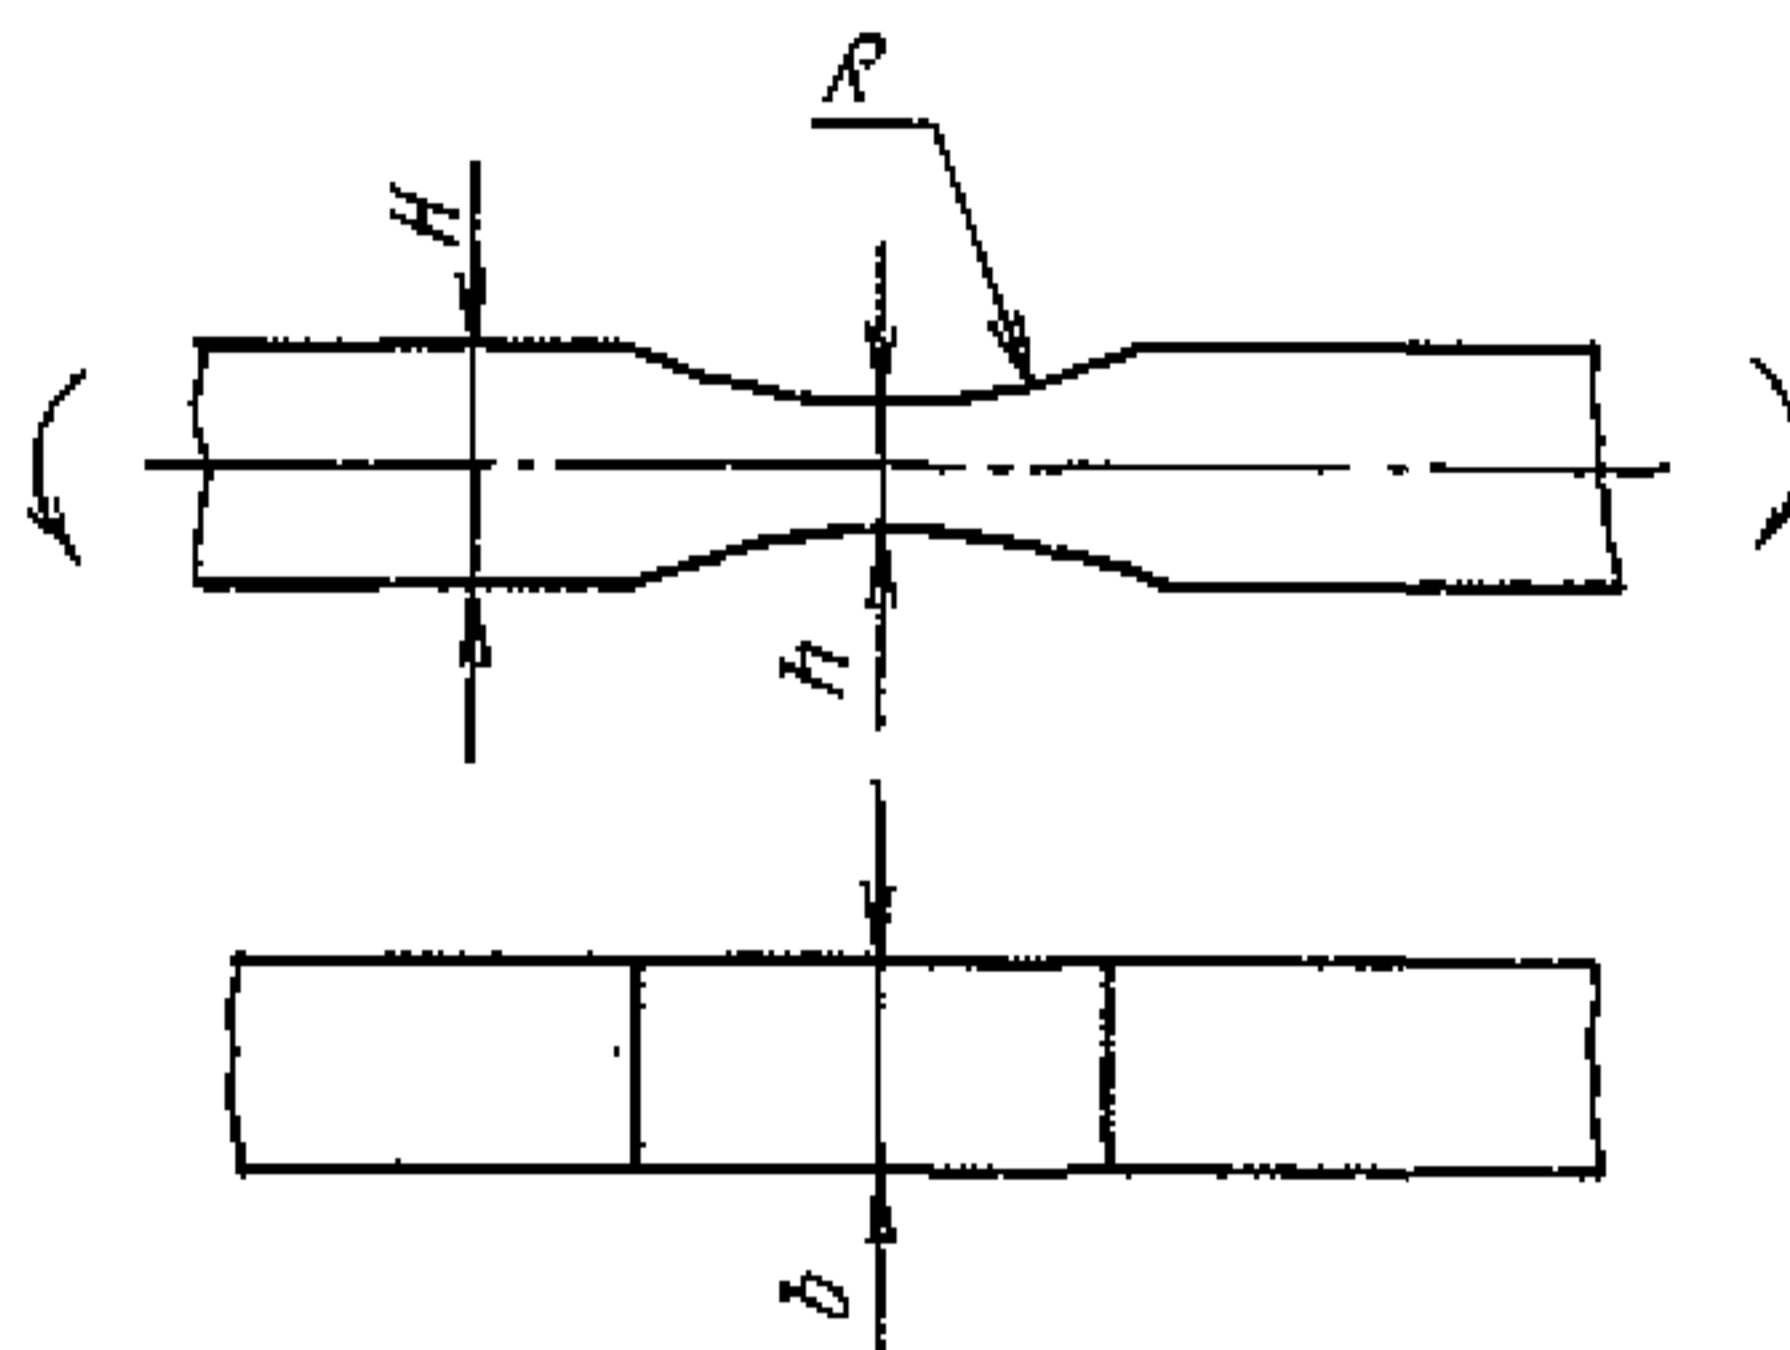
Форма и размеры рабочей части образца для испытаний при консольном изгибе:
